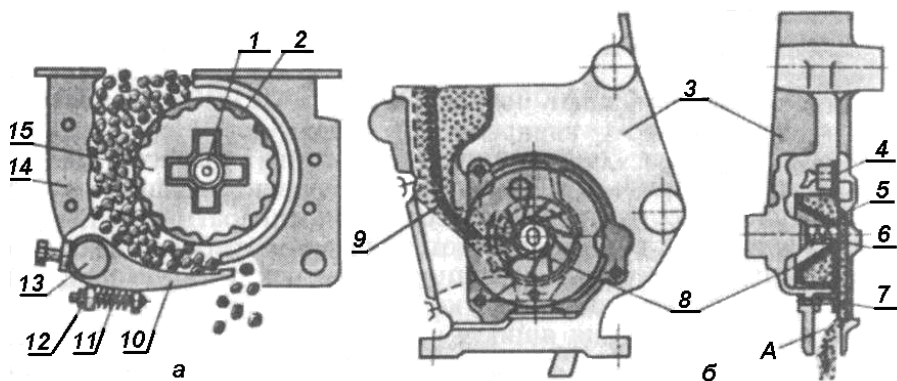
Разновидности катушечных высевяющих аппаратов: а – с разновеликими ребрами и клапаном с порошкой; б – катушечно-дисковый; 1, 13 – валы; 8, 15 – катушки; 2 – розетка; 3, 14 – корпуса; 4 – диск; 5 – окно; 6, 11 – пружины; 7 – болт заслонки; 9 – ворошилка; 10 – клапан; 12 – гайка
